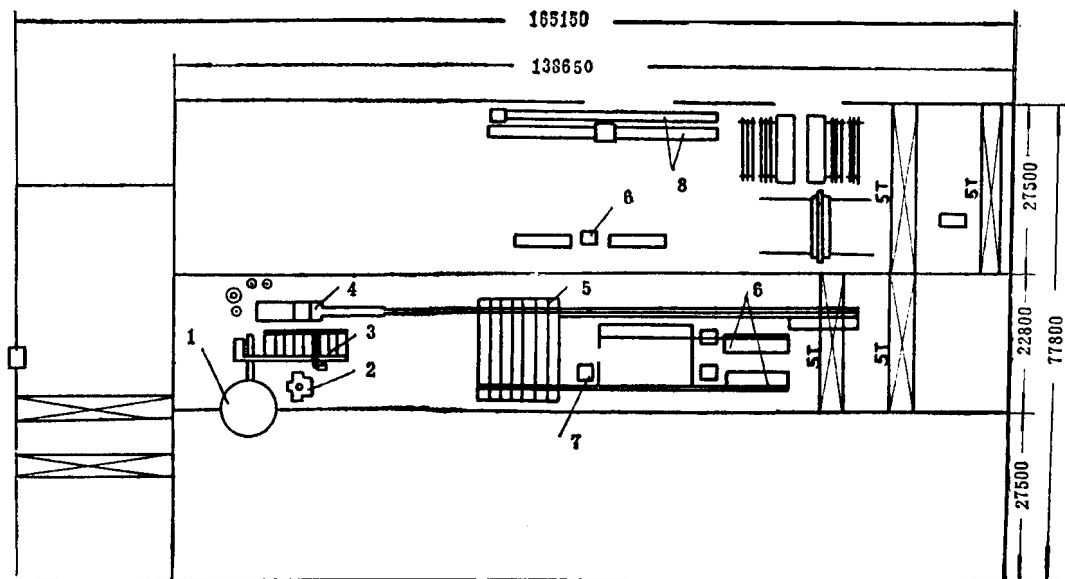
日本住友尼崎厂 2250 吨挤压机车间平面布置图
